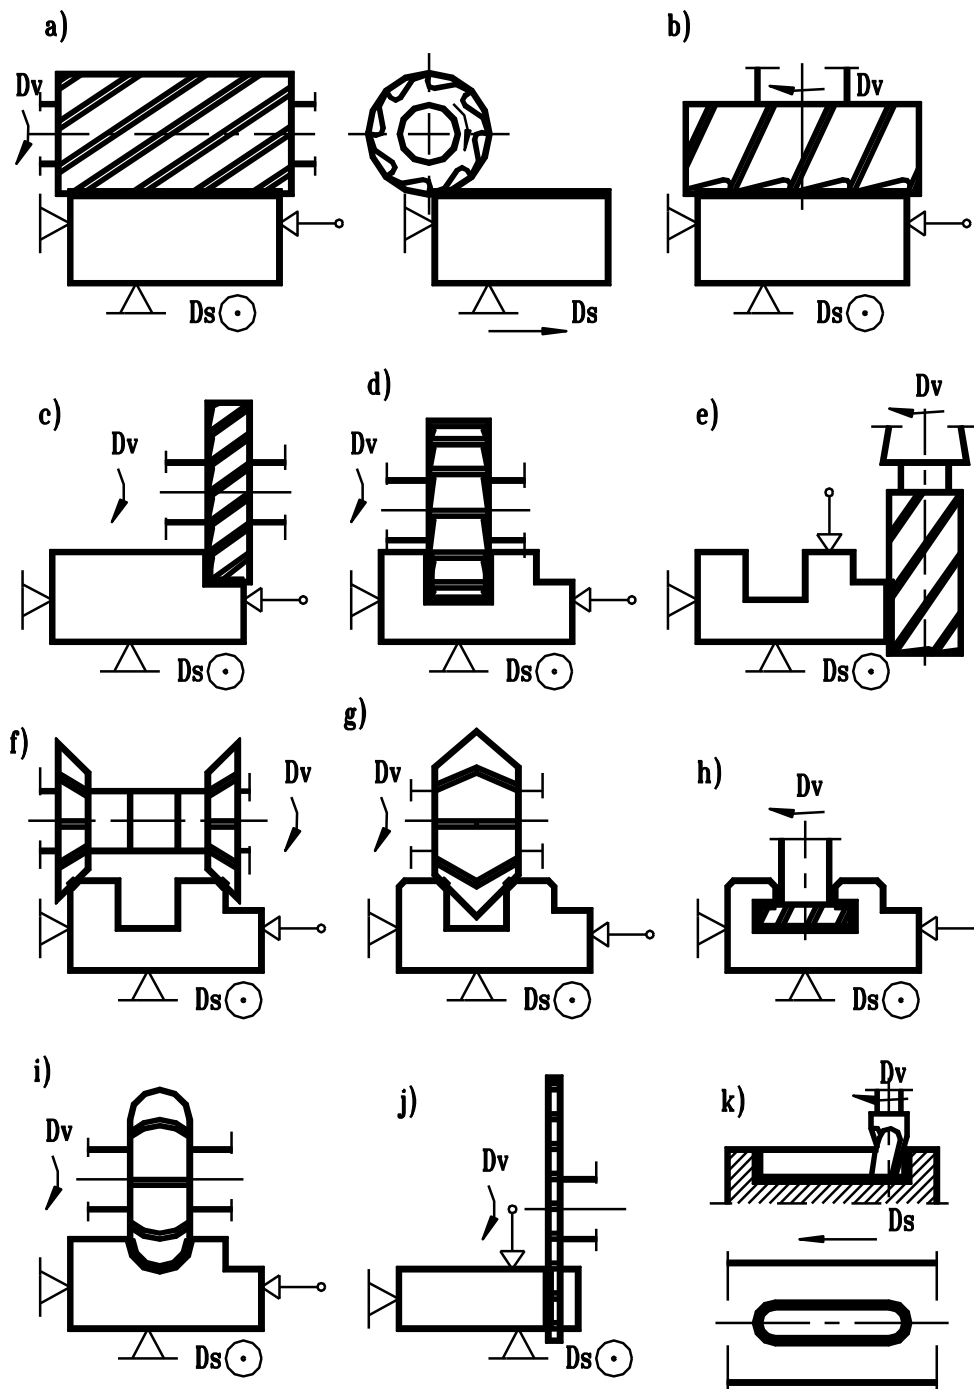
Esquemas principais de fresagem das superfícies diversas.
